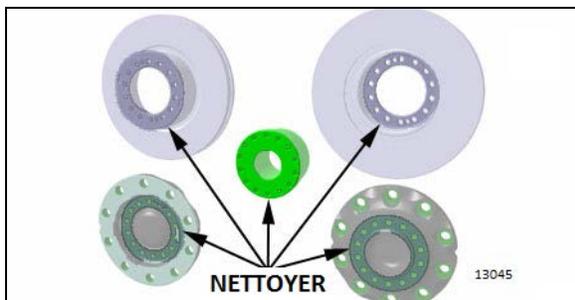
NETTOYAGE SURFACES DE SERRAGE DU ROULEMENT MOYEU/DISQUE/FLASQUE DU MOYEU
